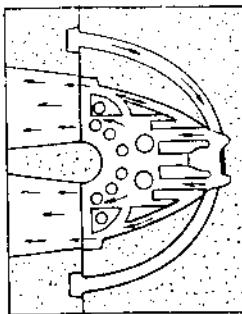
б. Схема формовки нижнего картера фланцем вверх, подвод металла из центрального литника под прибыль.
